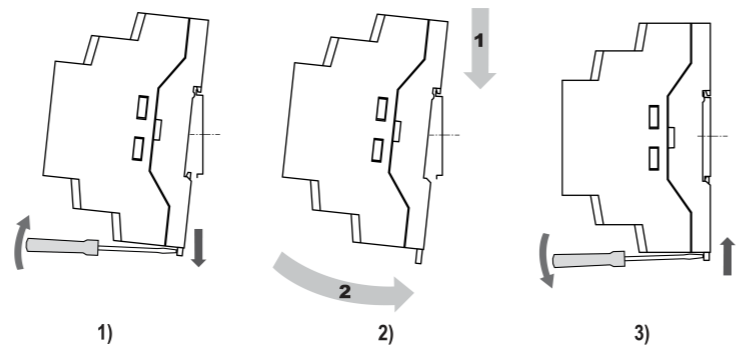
Монтаж прибора с креплением на DIN-рейку
